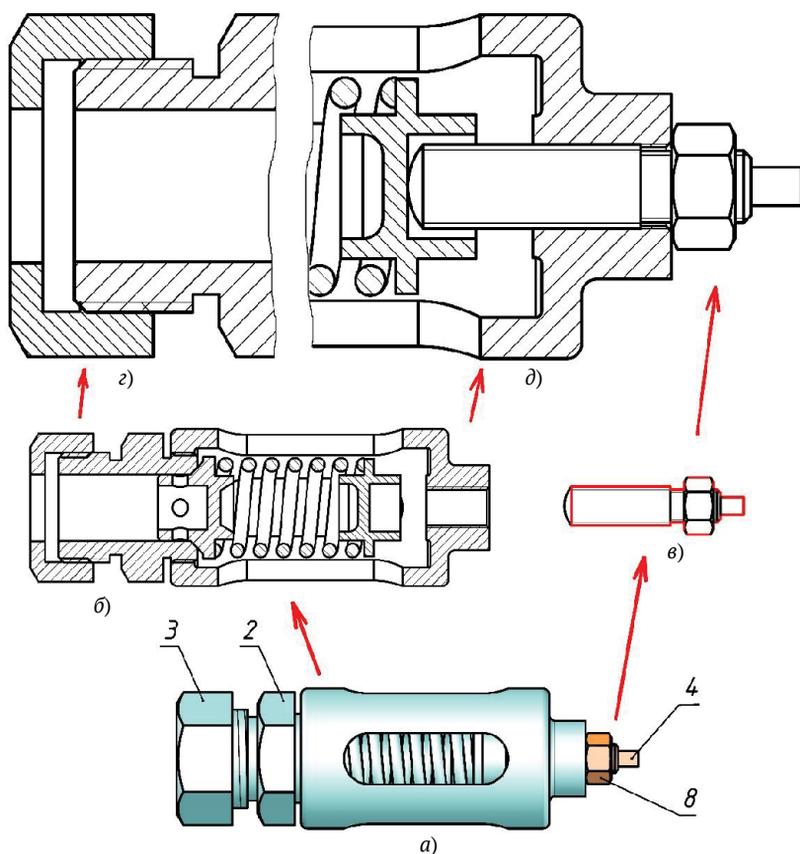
Схема построения разреза на сборочном чертеже:
